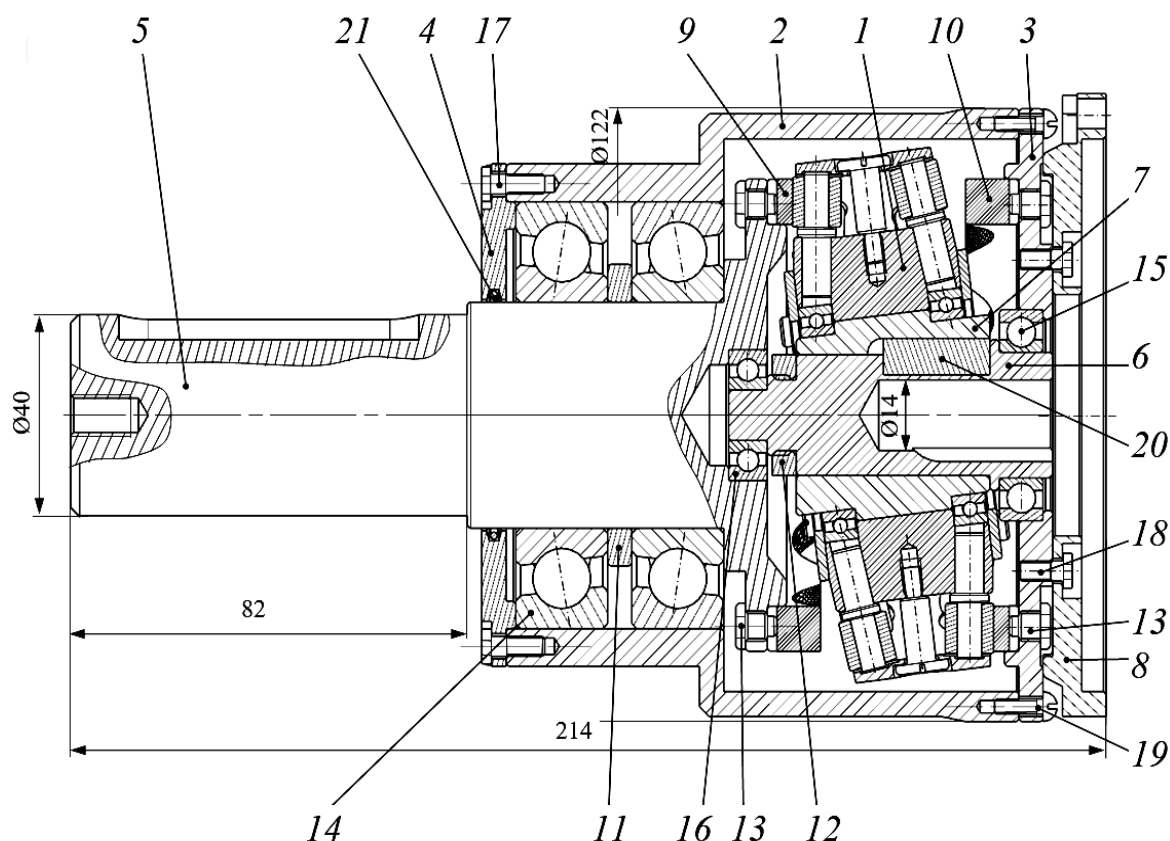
Общий вид редуктора с СРП с двухрядным сателлитом: 1 – сателлит; 2 – корпус; 3, 4, 8 – крышки; 5 – ведомый вал; 6 – ведущий вал; 7 – эксцентрик; 9, 10 – ведомое и остановленное центральные колеса; 11 – кольцо; 12 – гайка; 13 – регулировочный винт; 14–16 – подшипники качения; 17–19 – винты; 20 – шпонка; 21 – уплотнение
